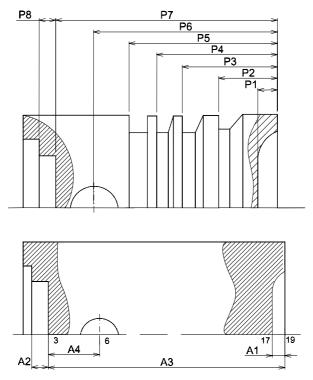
Эскизы детали и заготовки с условными обозначениями размеров
